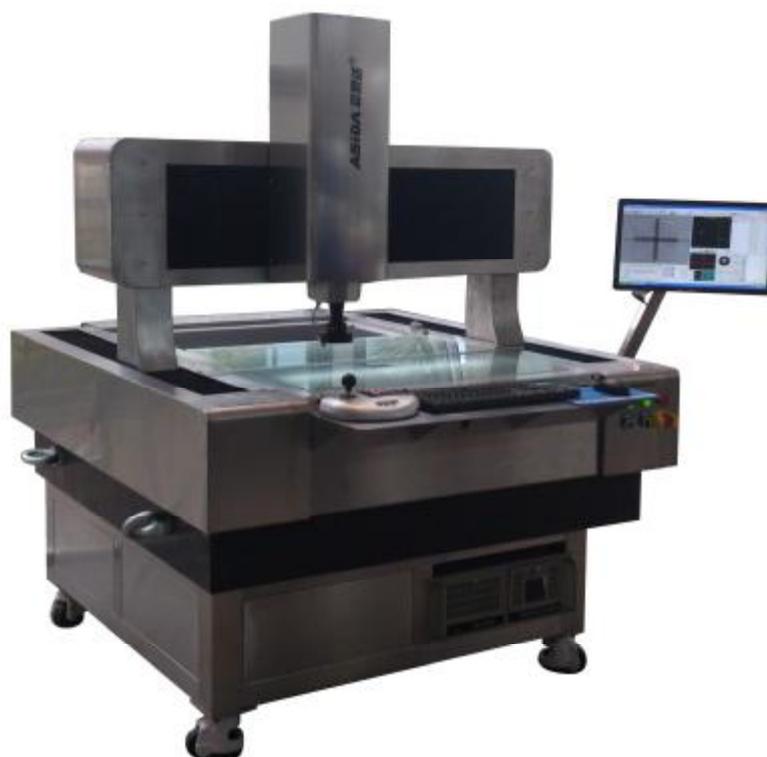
Внешний вид приборов для автоматического измерения размеров печатных плат и фотошаблонов IMM
